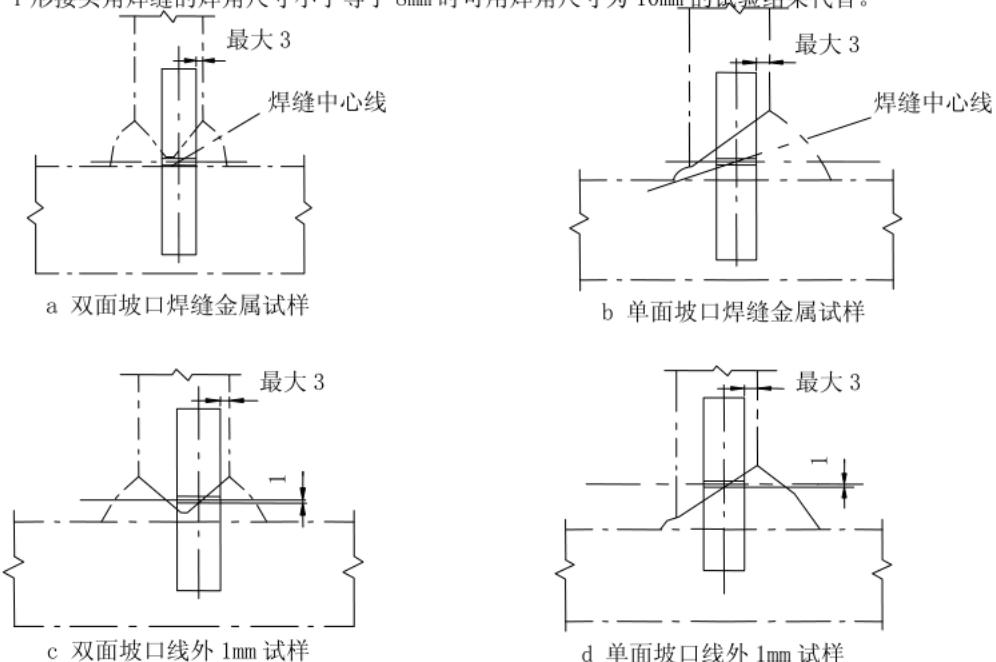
T 形对接熔透焊缝的冲击试样取样
